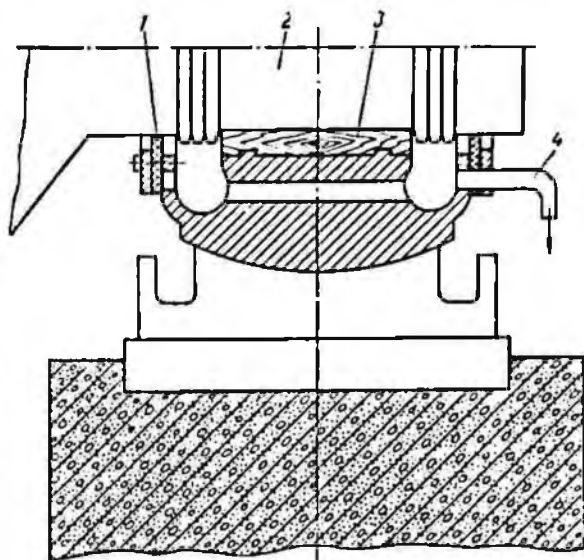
Схема расположения вкладыша в корпусе подшипника:
